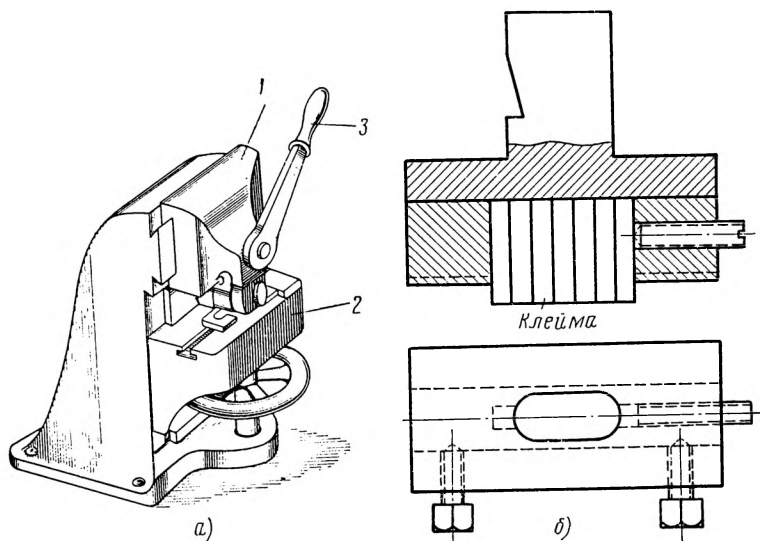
Станок для маркировки изделий накаткой (а), державка с клеймами для маркировки изделий (б).
